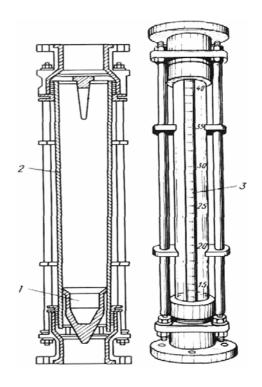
Ротаметр местного измерения показаний: 1 — поплавок; 2 —коническая трубка; 3 — шкала
